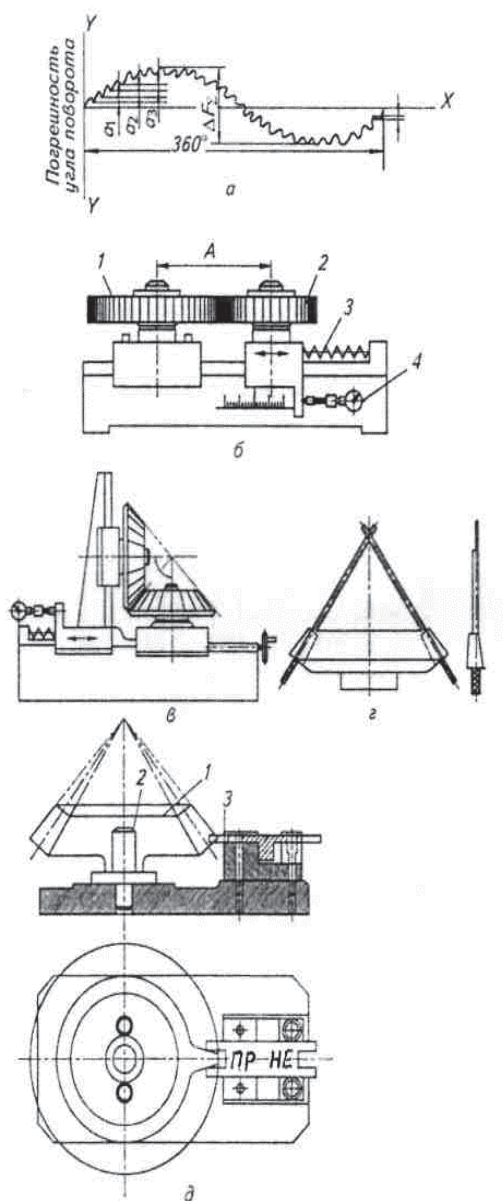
Контроль зубчатого зацепления: а – график кинематической погрешности; б – прибор для проверки цилиндрических колес без бокового зазора в зубьях; в – прибор для проверки конических колес без бокового зазора в зубьях; г – проверка направления зубьев конического колеса; д – проверка толщины зуба конического колеса: 1 – коническое колесо; 2 – установочный штырь; 3 – калибр, пр – проходной, не – непроходной; 4 – индикатор
